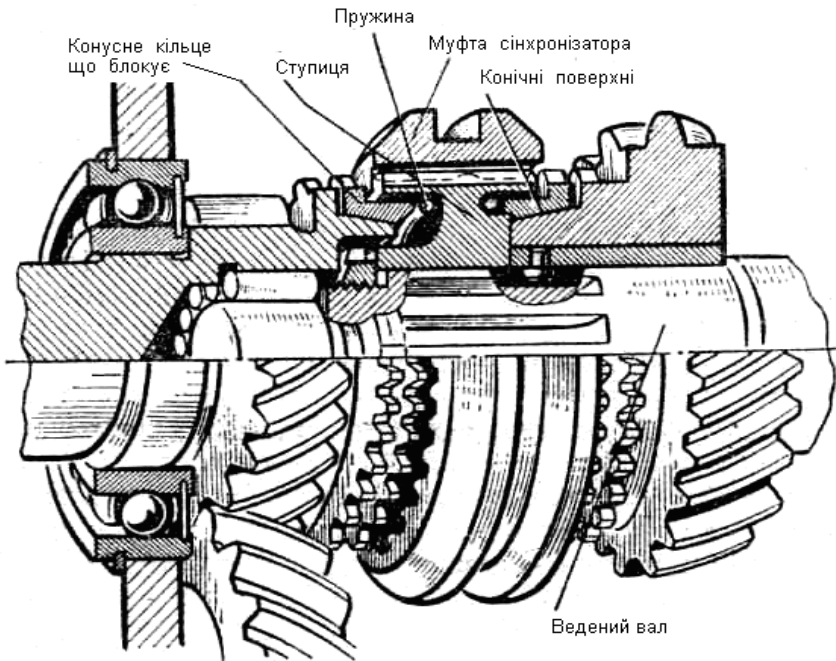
Синхронізатор коробки передач автомобіля ГАЗ-53А
